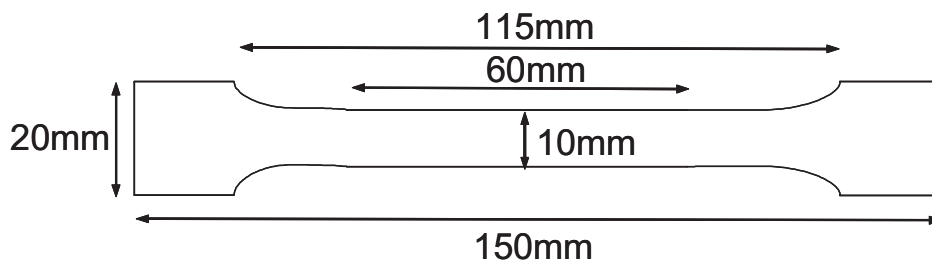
Dimensions des éprouvettes de PU et de résine époxy.
